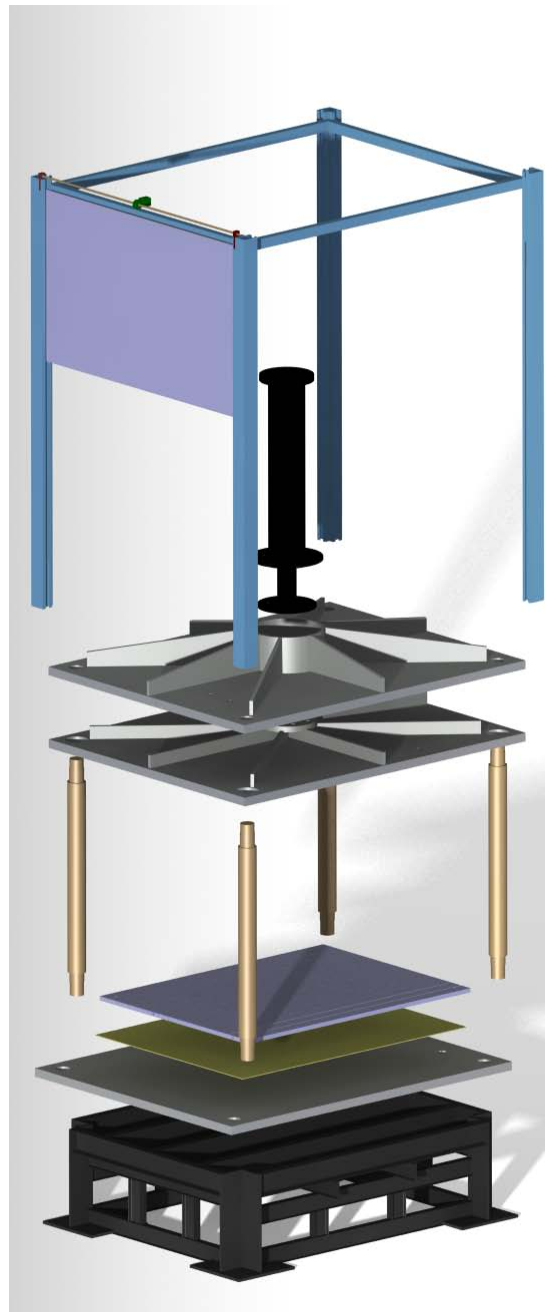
Despiece de los elementos principales de la prensa de platos calientes.
